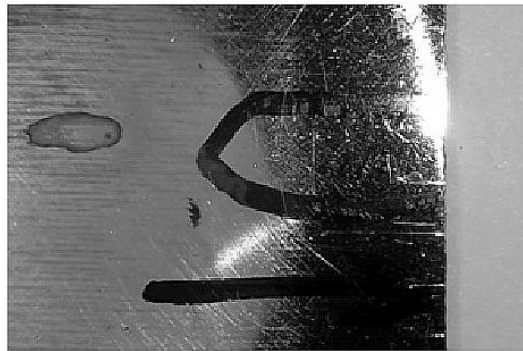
Зона измерения твердости от ОМ к ЗТВ сварного шва.
